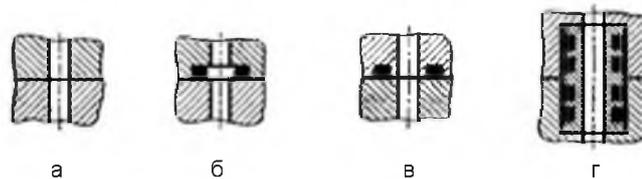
Схемы соединения гидролиний при плоской стыковке двух деталей
